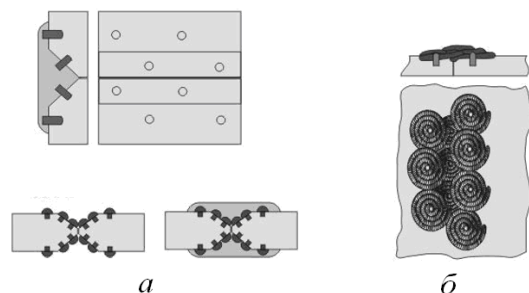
Сварка чугуна с постановкой стальных шпилек:
